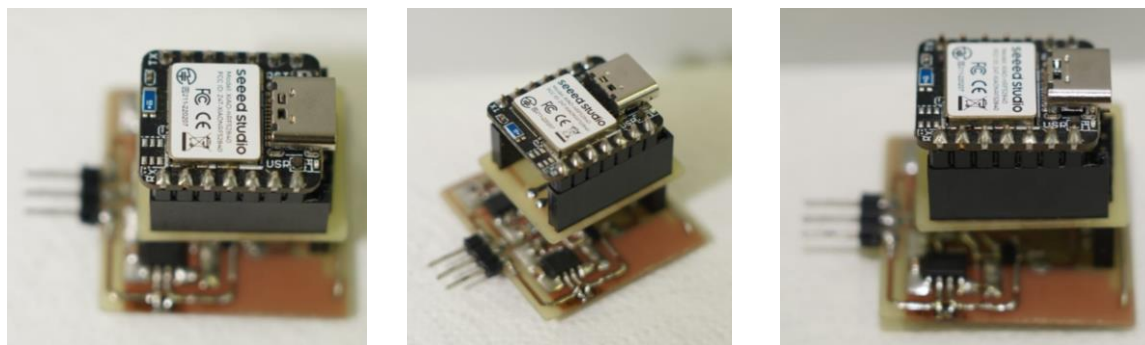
Connexió amb adaptador entre la PCB i el XIAO.
